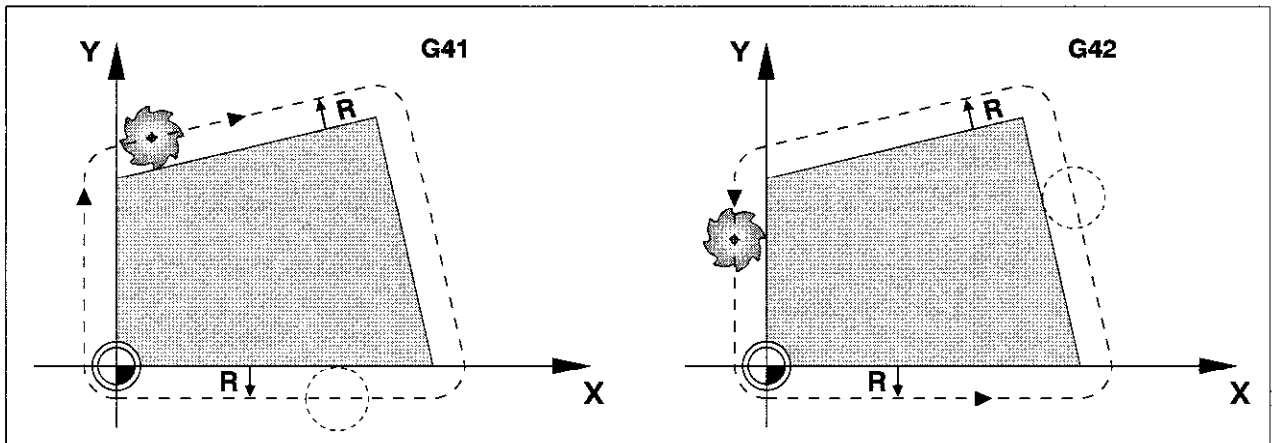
Das Werkzeug verfährt zum Fräsen links (G41) oder rechts (G42) von der Kontur
